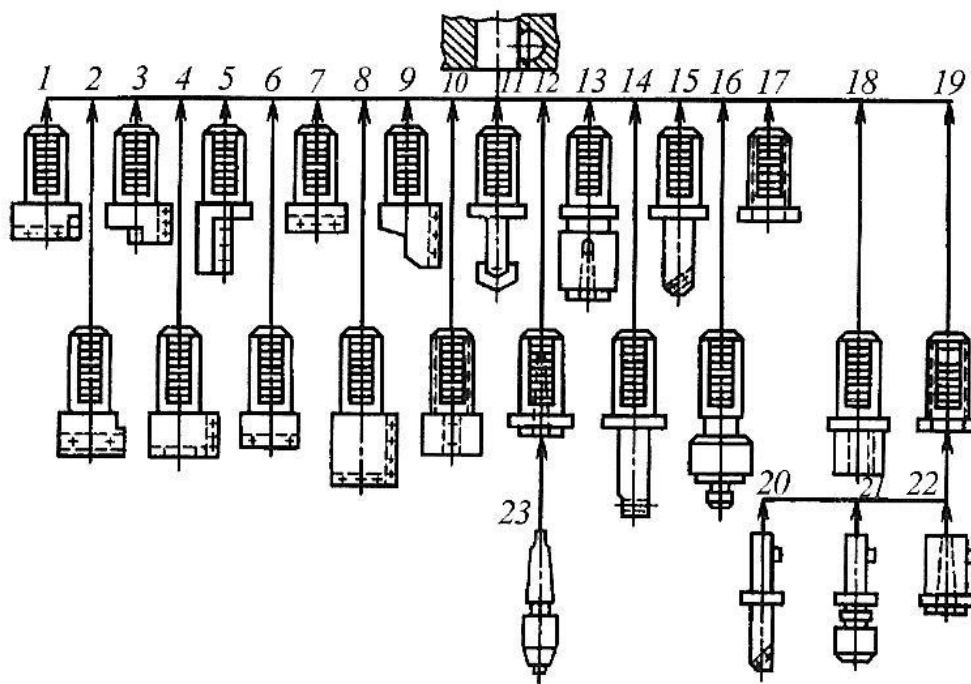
Конструкция резцедержателя с цилиндрическим хвостовиком
